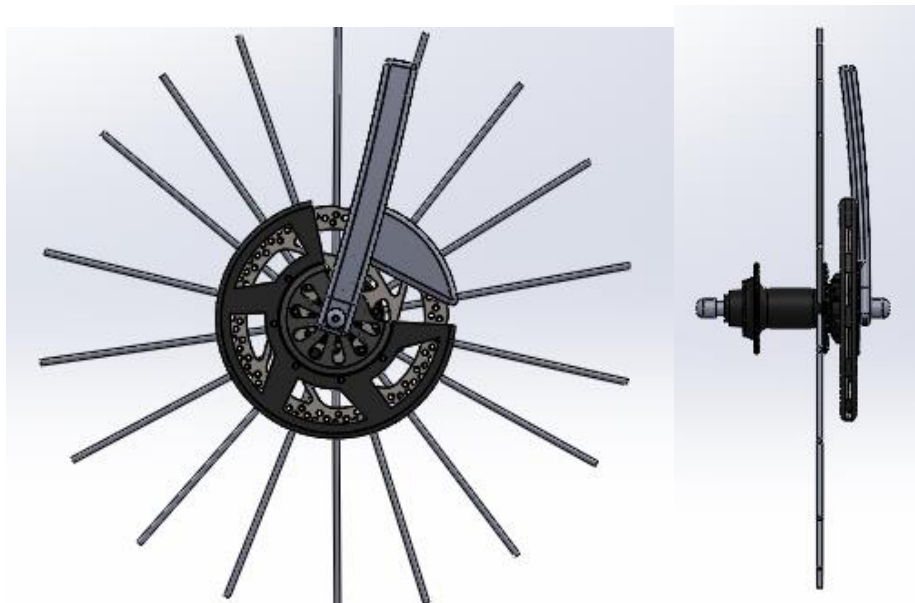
Vista del conjunto de los elementos de contorno ensamblados de la parte delantera.
